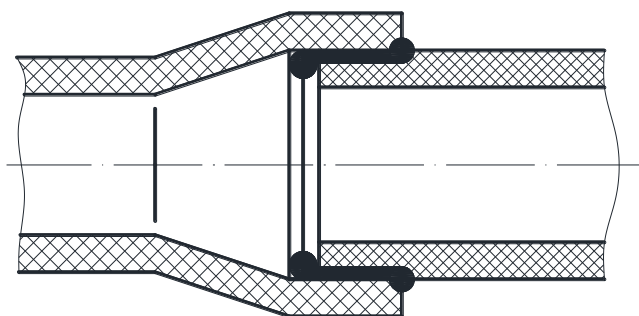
Конструктивные элементы шва сварного соединения (шов Н1)
